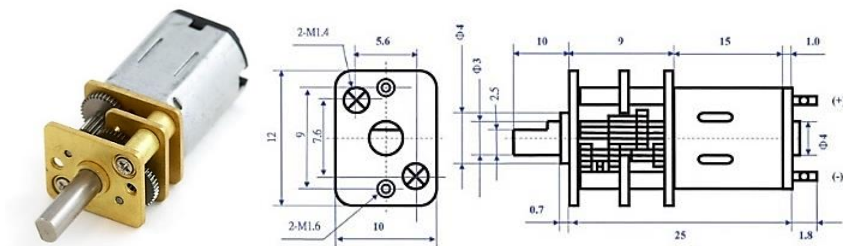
Мотор-редуктор Gekko MR12-050
